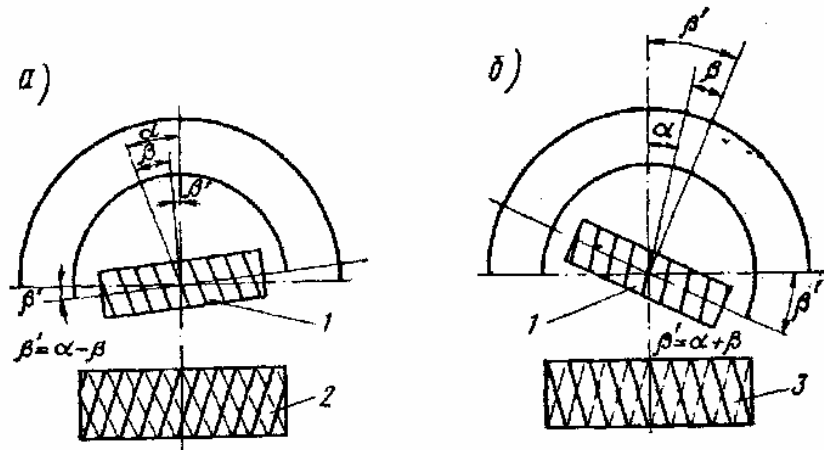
Установка червячной фрезы при зубонарезании цилиндрических зубчатых колес с косым зубом: 1 – правозаходная фреза; 2 – заготовка правозаходного зубчатого колеса; 3 – заготовка левозаходного зубчатого колеса.
